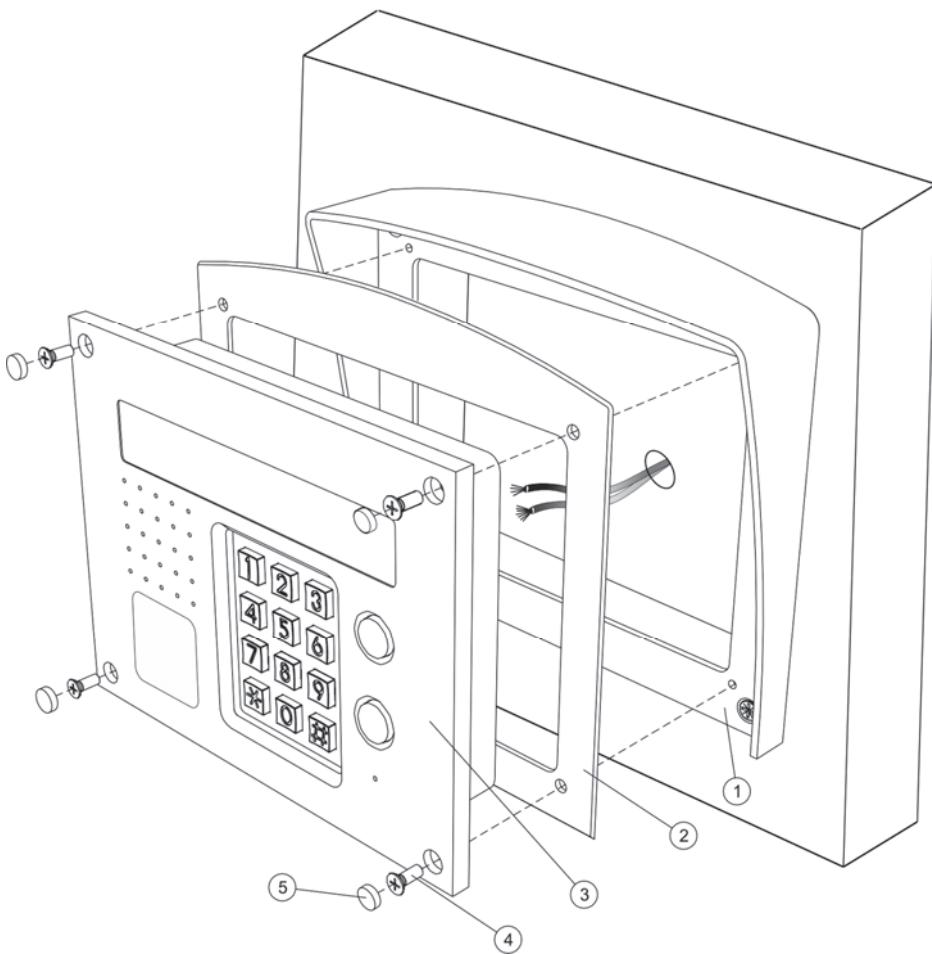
Установка блока вызова на наподвижной части металлической двери
